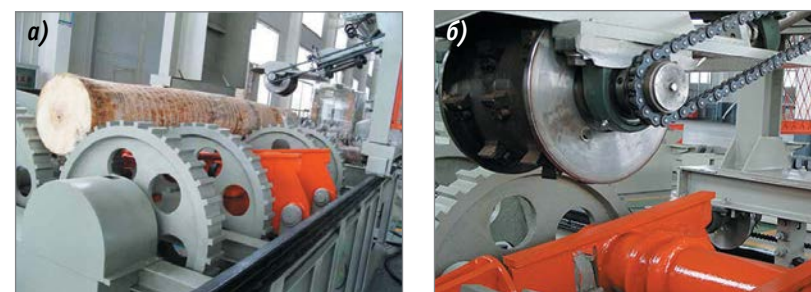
Окорочный станок ВВР1413 (а) с окоривающей фрезой (б)
